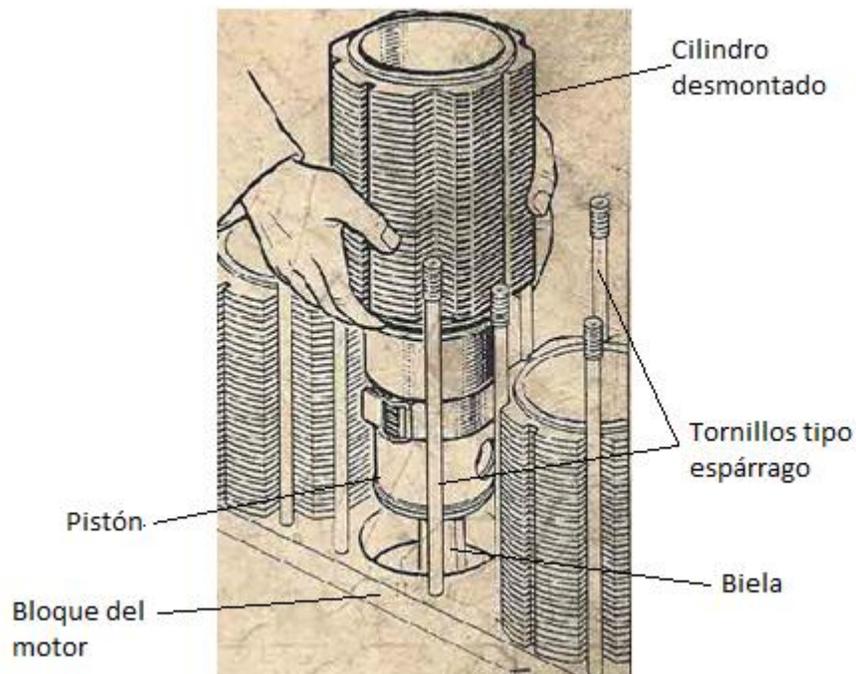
Bloque de motor y partes que lo conforman. Fuente: Documento plan de engrase para motores Dieselair 120 y Agrom, 1967.
